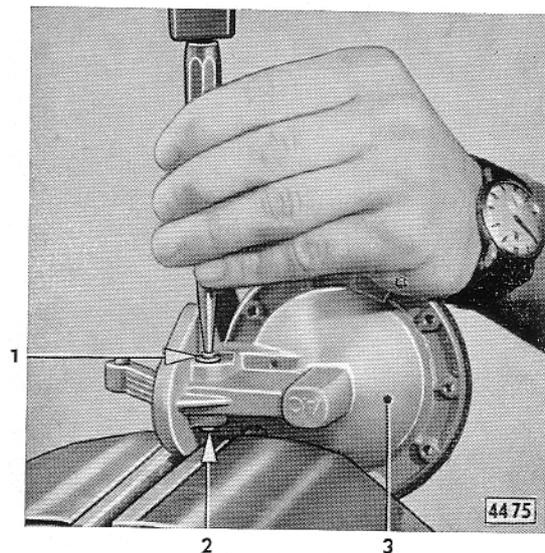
Lagerbolzen für Kipp- und Schwinghebel aus Gehäuse ausschlagen
